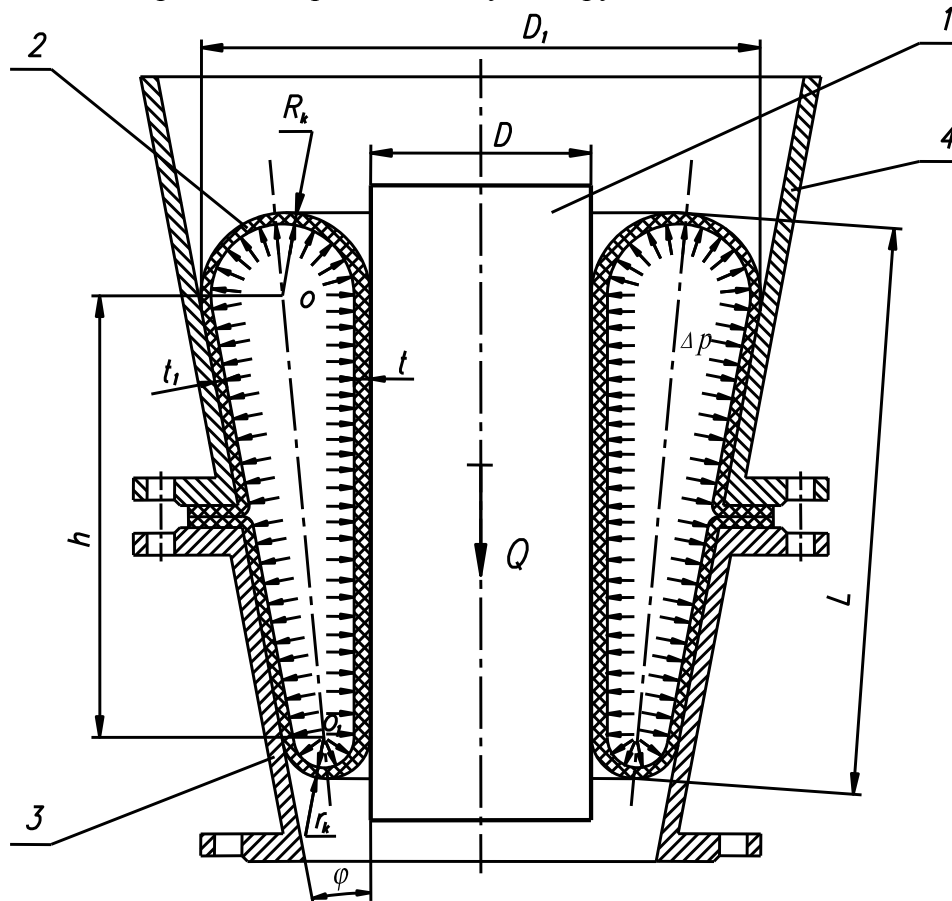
1 – жёсткий цилиндр (груз), 2 – конический эластичный тор, 3,4 – корпуса рабочей камеры.
